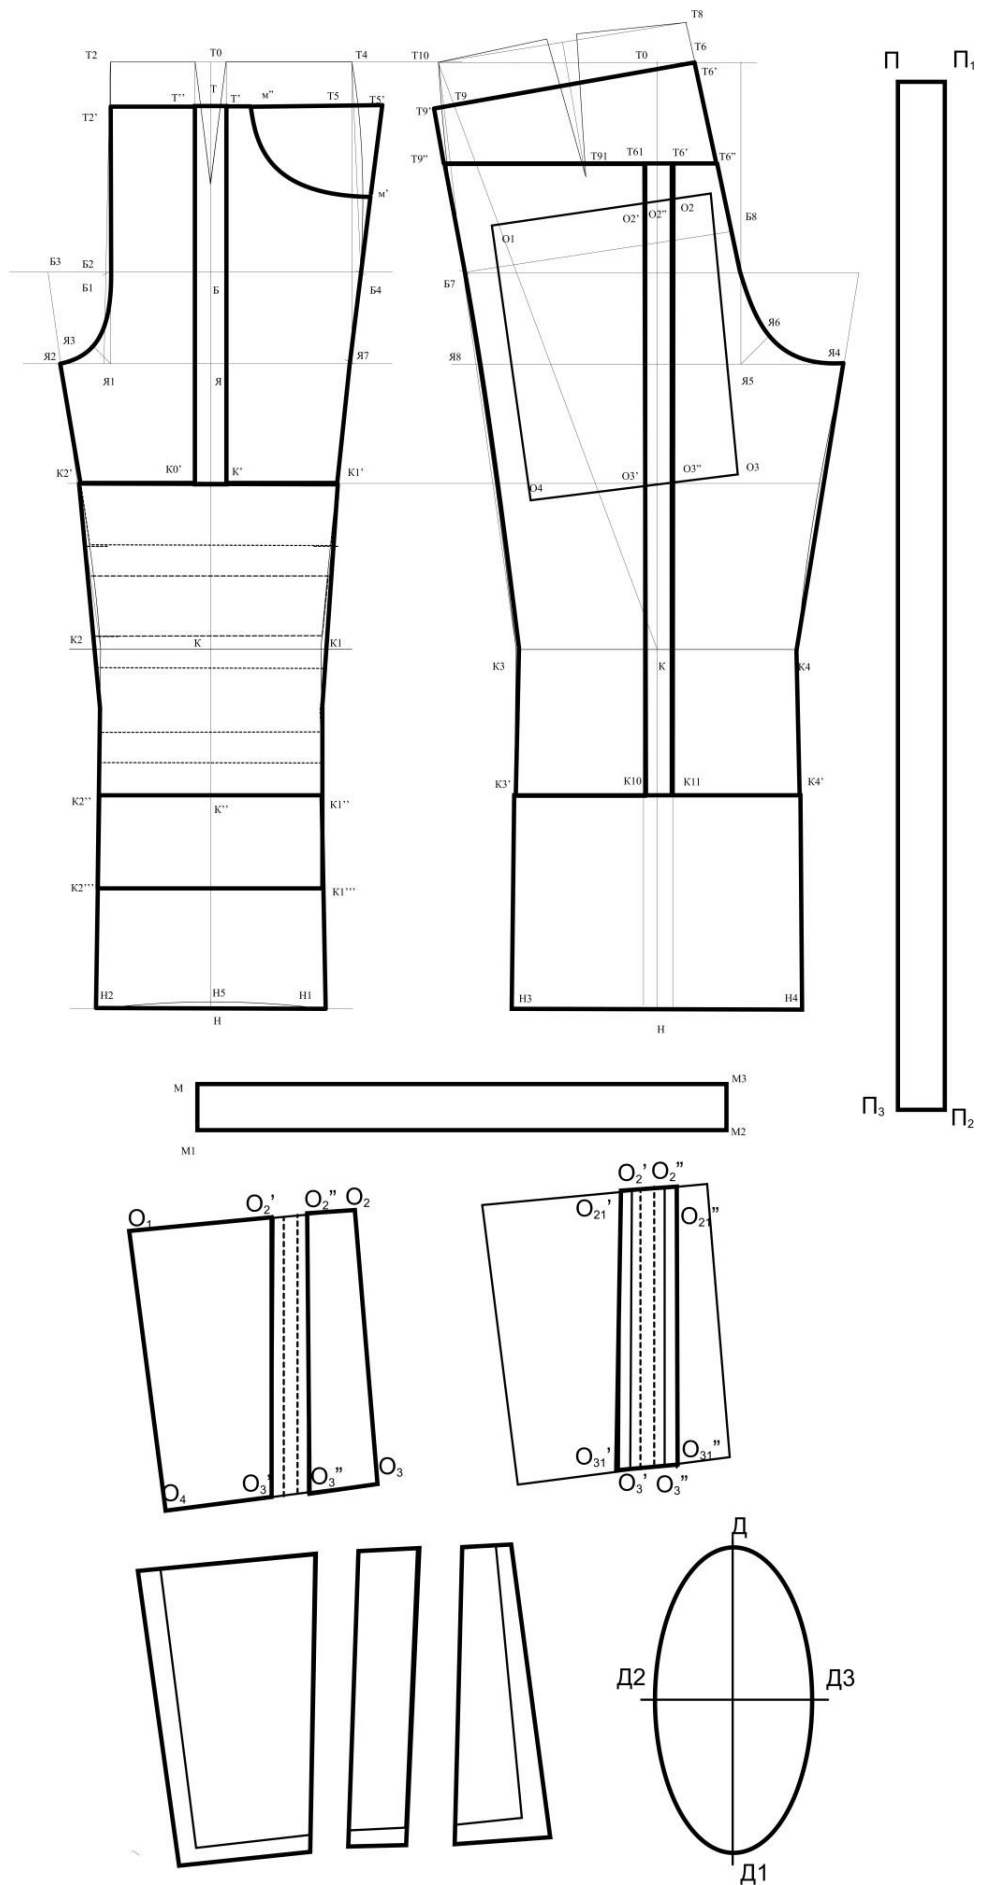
Схема креслення базової конструкції штанів дитячих
